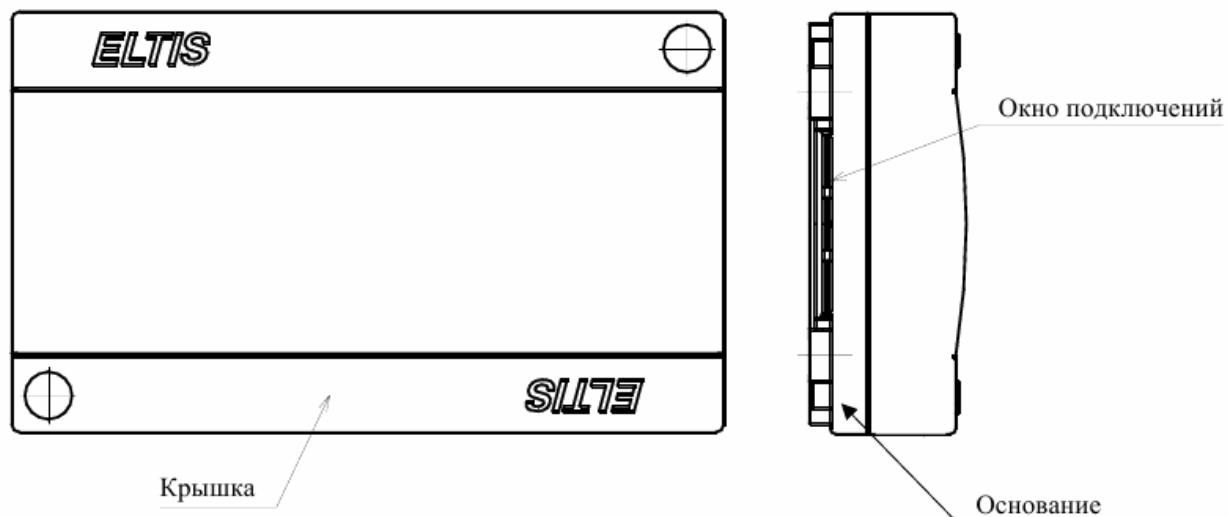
Внешний вид коммутатора KMV1.4-2.4
